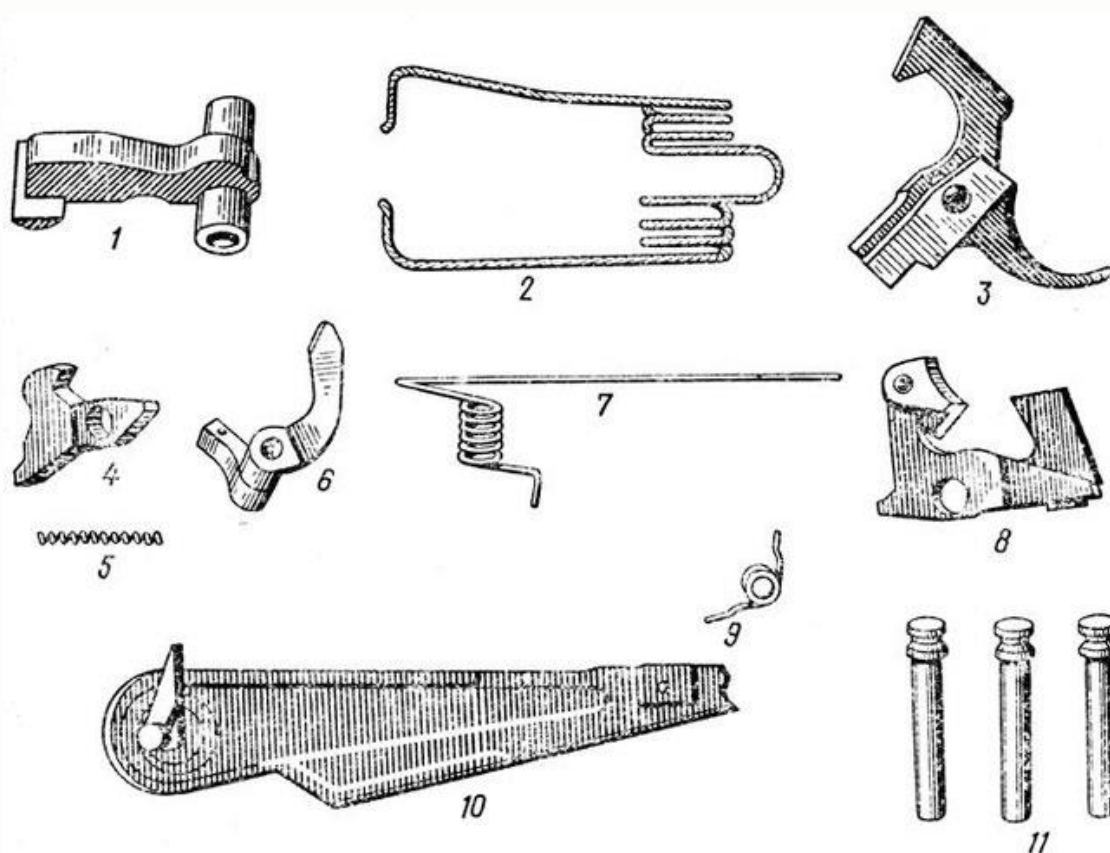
Ударно-спусковой механизм: 1 — курок; 2 — боевая пружина; 3 — спусковой крючок; 4 — шептало одиночного огня; 5 — пружина шептала одиночного огня; 6 — автоспуск; 7 — пружина автоспуска; 8 — замедлитель курка; 9 — пружина замедлителя курка; 10 — переводчик; 11 — оси
